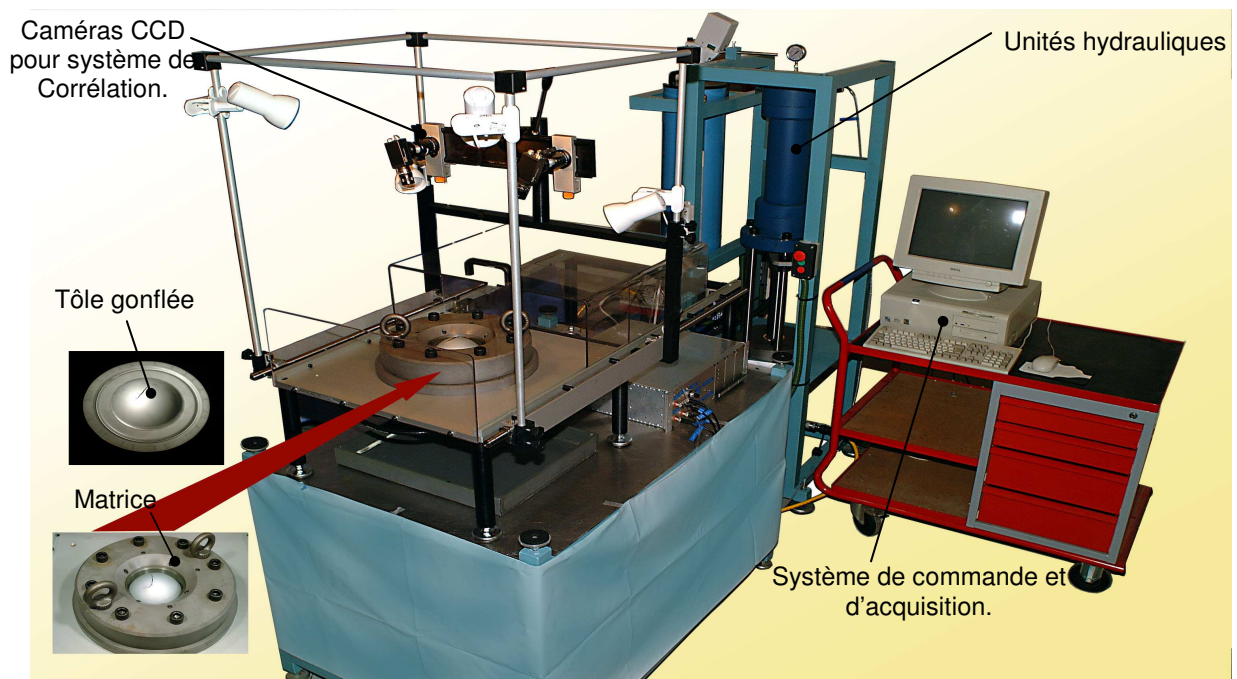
Vue d'ensemble de la machine de gonflage.
